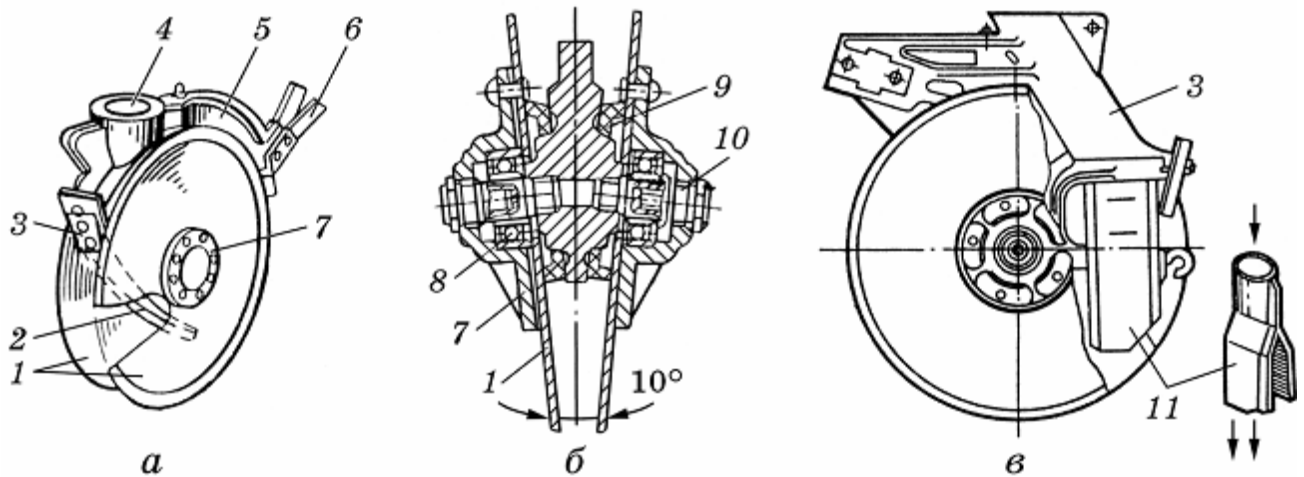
Сошники дискові: а і б — дводисковий однорядковий; в — дводисковий дворядковий; 1 — диски; 2 — напрямна пластина; 3, 14 і 17 — чистики; 4 — розтруб; 5 — корпус; 6 — повідець; 7 і 13 — маточини; 8 — підшипник; 9 — ущільнювач; 10 — вісь; 11 — розподільна лійка; 12 і 20 — лійка; 15 і 23 — кронштейни; 16 і 19 — реборди; 18 — грудковідвід; 21 — дисковий ніж; 22 — підвіска; 24 — сошник.
